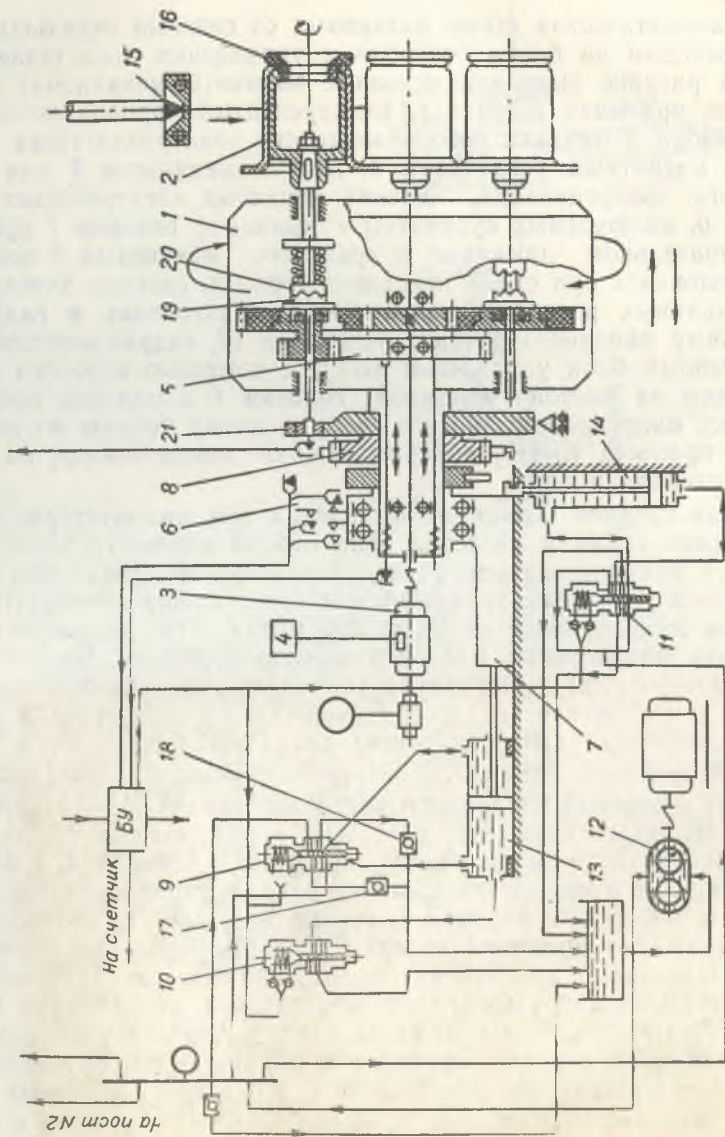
Кинематическая схема механизма подачи шихтового металла установки типа АЛМ-5
